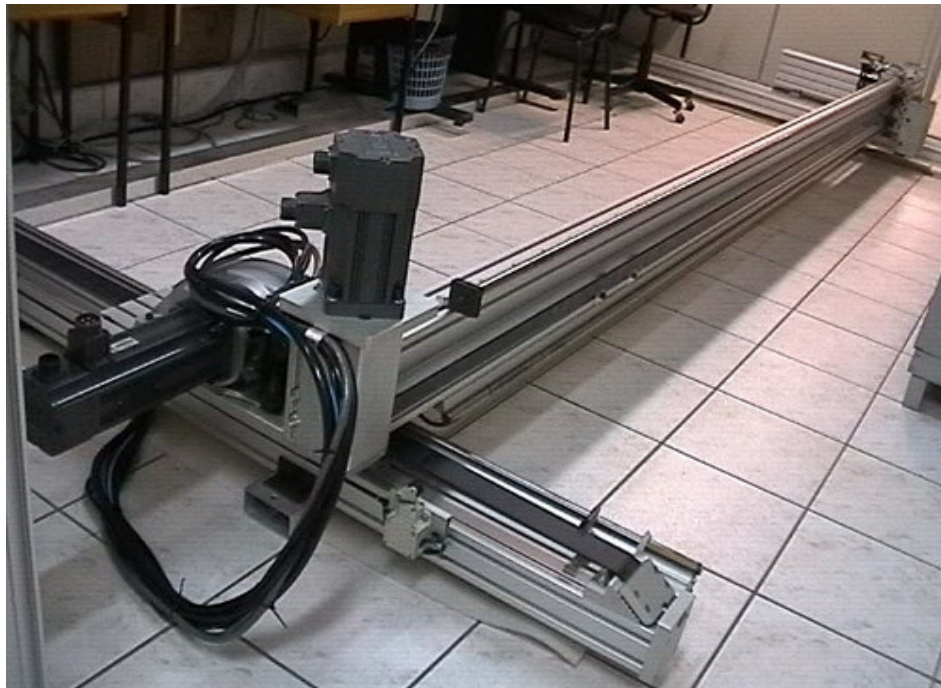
Estrutura mecânica do protótipo do Conjunto Impressor.
